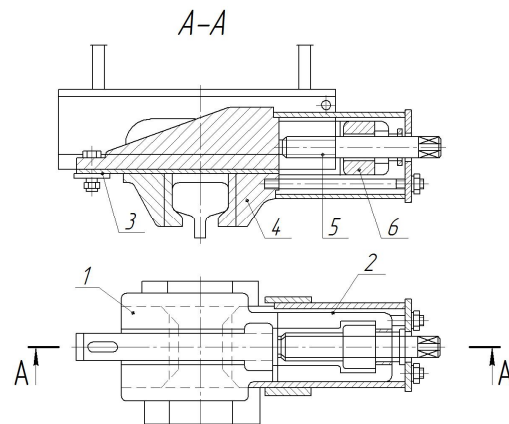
Рельсовый захват с нижним расположением винта:
